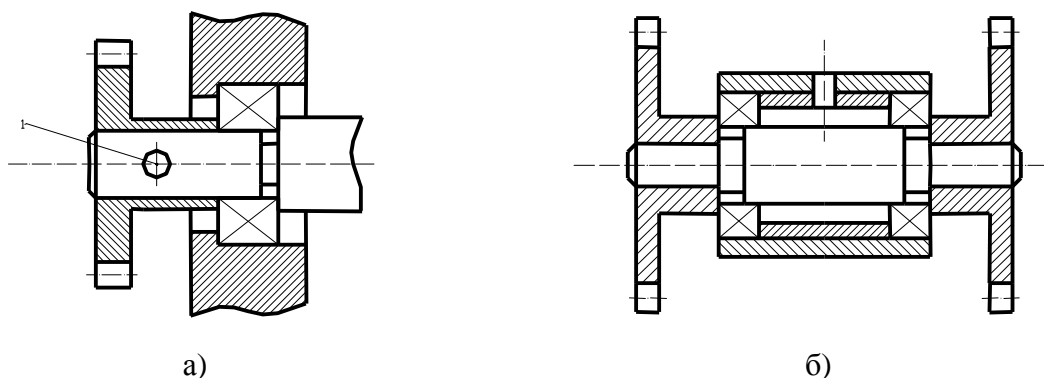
Вузлове кріплення підшипників: а – консольне кріплення зубчастого колеса; 1 – штифт; б – кріплення двох зубчастих коліс на підшипниковій стійці; між підшипниками встановлено кільце, що штифтом фіксується від поздовжніх переміщень
